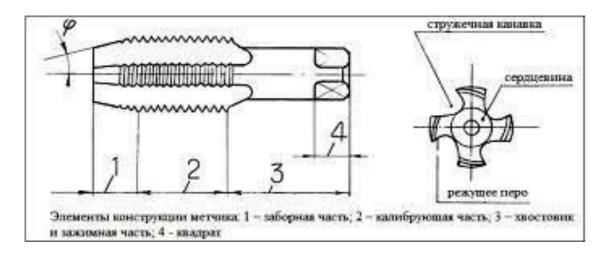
Метчик: 1— заборная часть; 2 — калиброванная часть; 3 — хвостовик; 4 — квадрат
